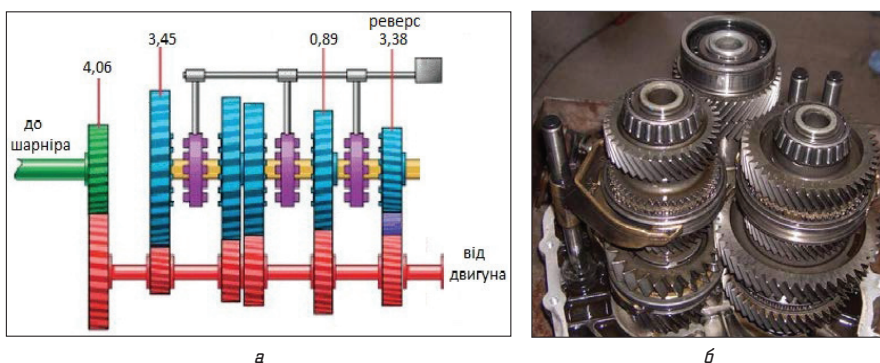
Схема передавальних відношень редуктора із зубчатыми циліндричними передачами та з реверсною передачею (а); внутрішній вигляд редуктора 084 5F AKW (б)
